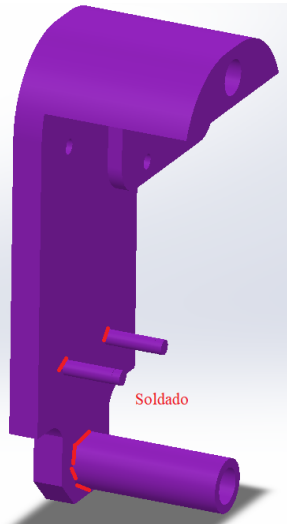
Vista de montaje de pieza N°6 en la parte superior de la estructura (Fuente 93)
